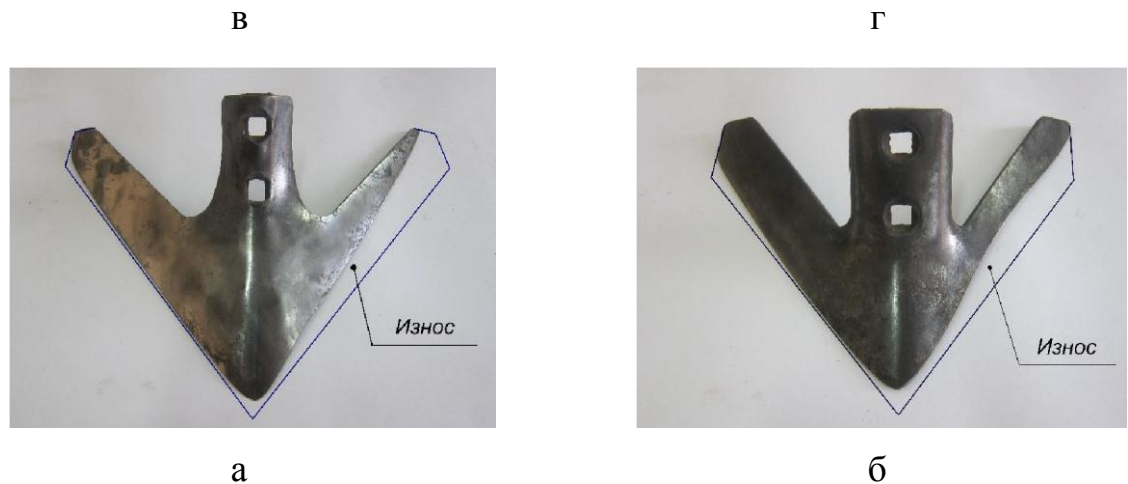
Робочі органи, що мають нерівномірне зношування крил [2]: а - лапа культиватора КШУ-12Н; б - посівний комплекс John Deere 730.
